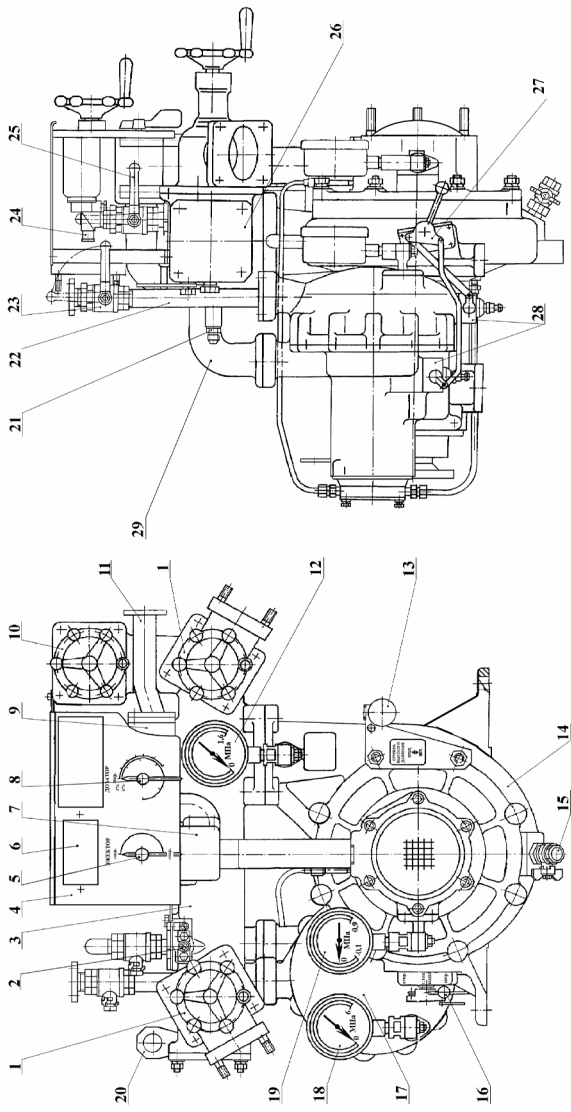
Насос центробежный пожарный комбинированный НЦПК-40/100-4/400
